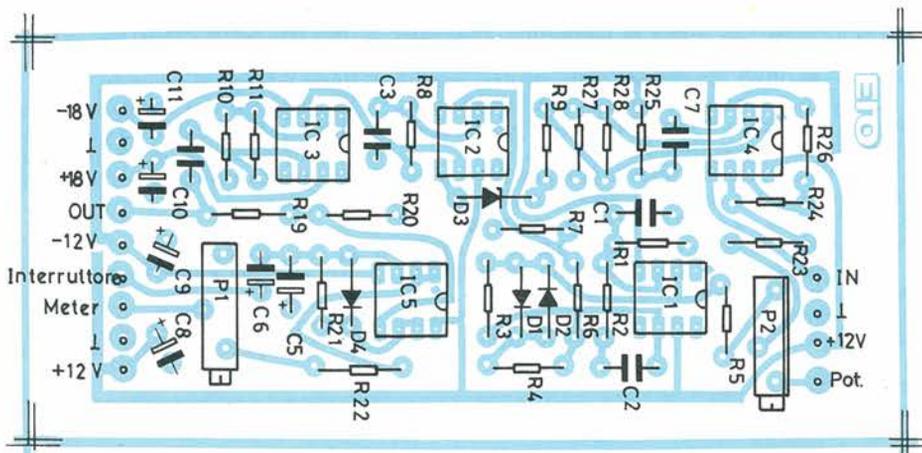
Disposizione dei componenti sul circuito stampato del Millivoltmetro.
